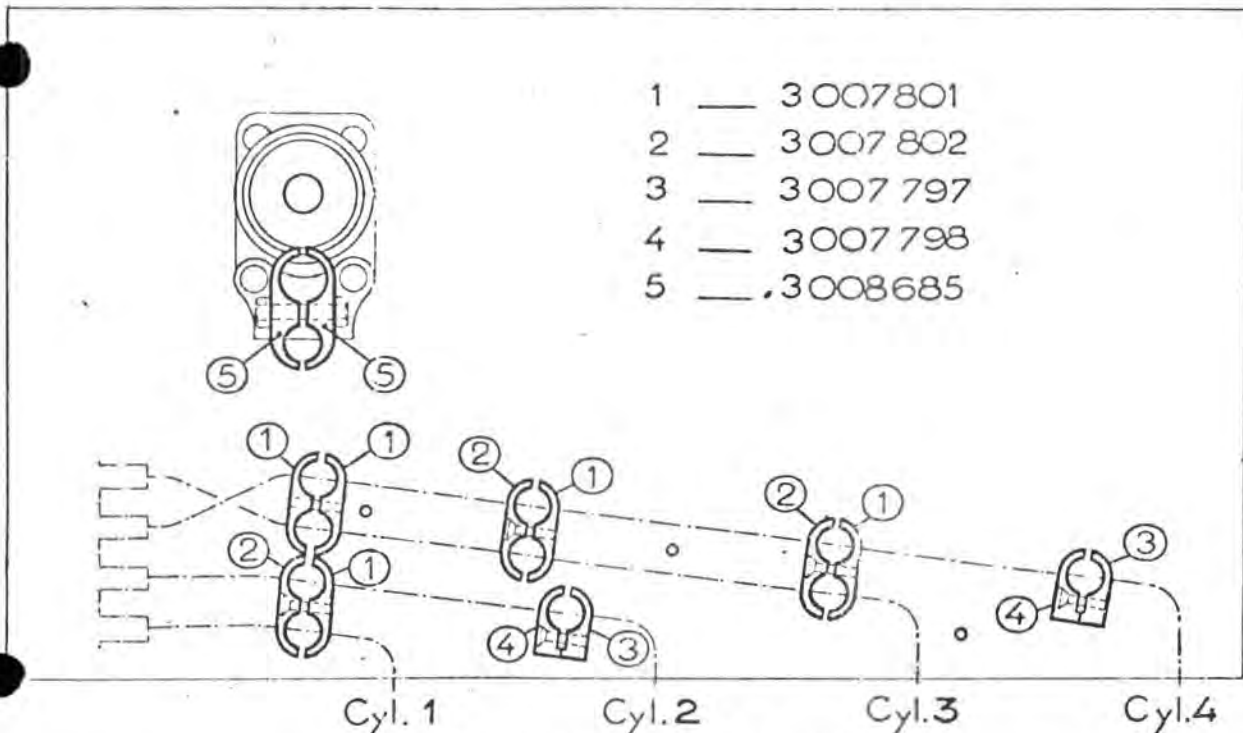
MONTAGE DES TUBES DE DÉMARRAGE
